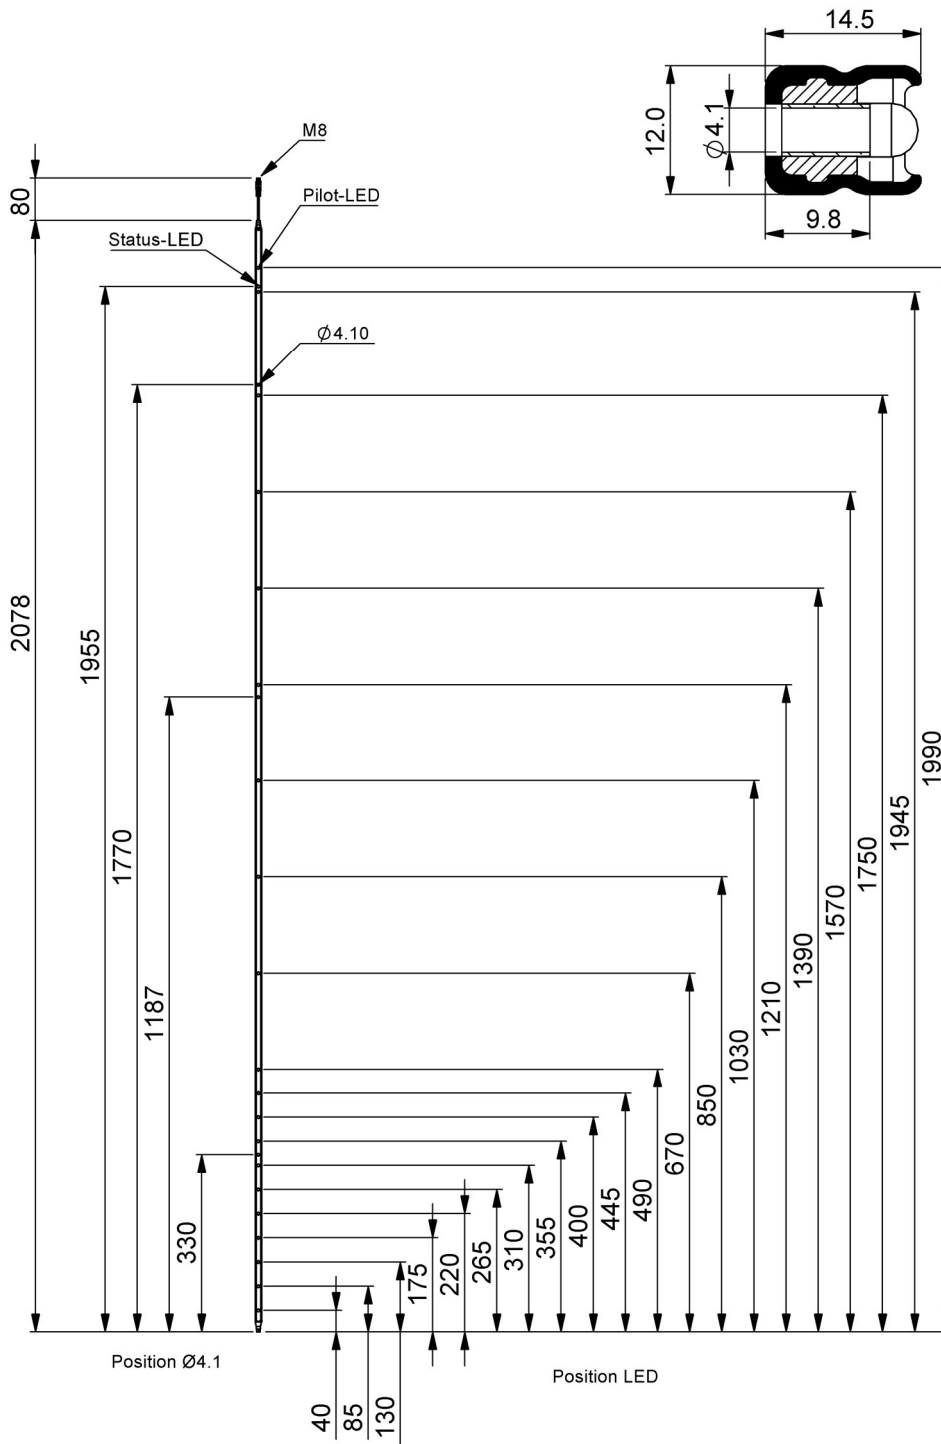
RAY-LG 3520 Dimensionen (mm)
